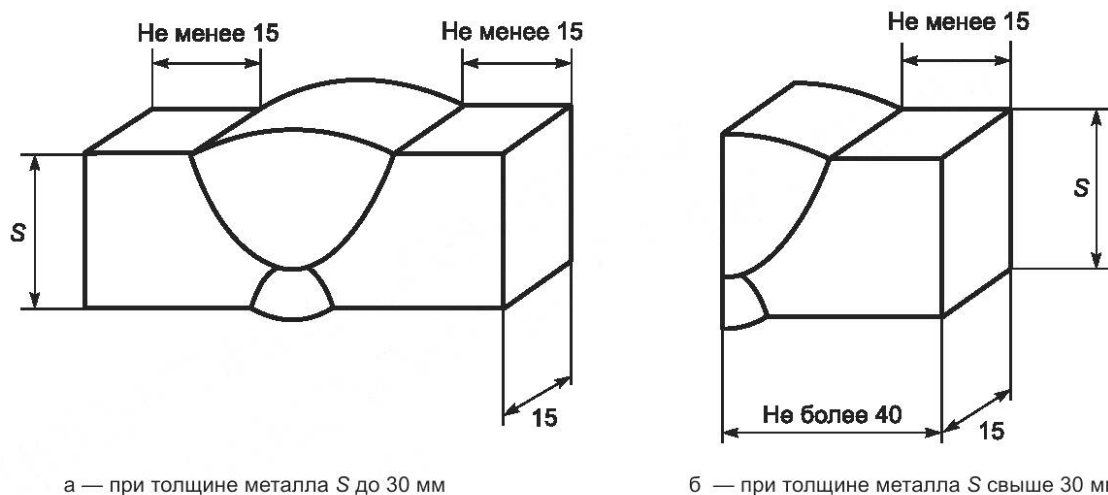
Размеры образцов для металлографических исследований макроструктуры сварных соединений
